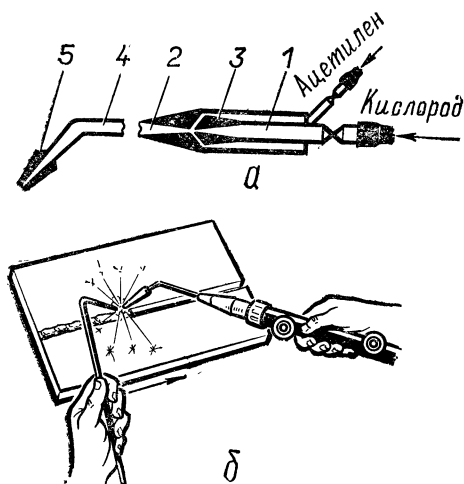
Схема кислородно-ацетиленовой: а) сварочной горелки; б) газовой сварки.
